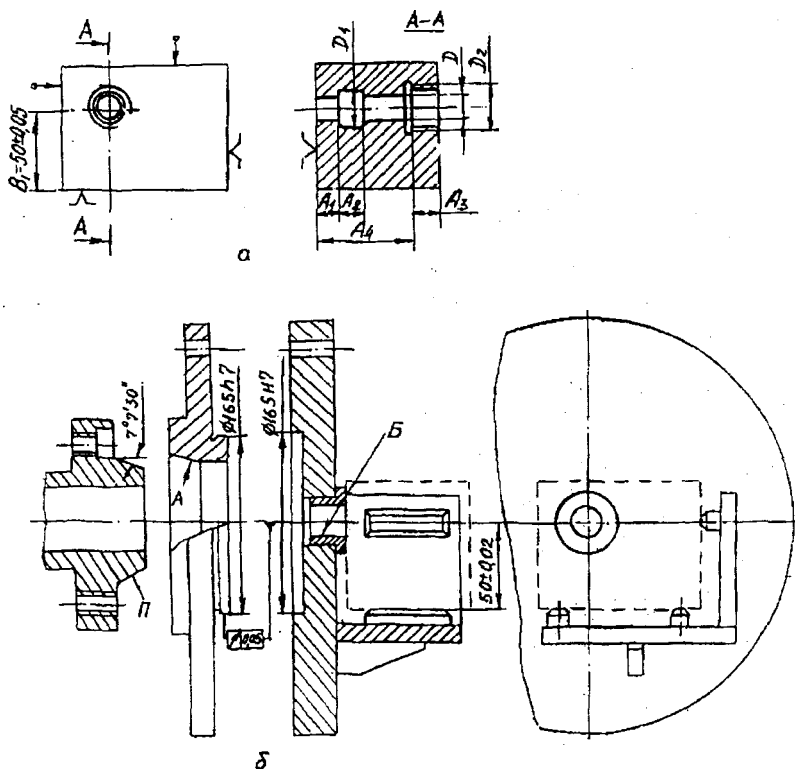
К расчету точности обработки в приспособлении на револьверном станке: а – операционный эскиз; б – конструктивная схема приспособления
